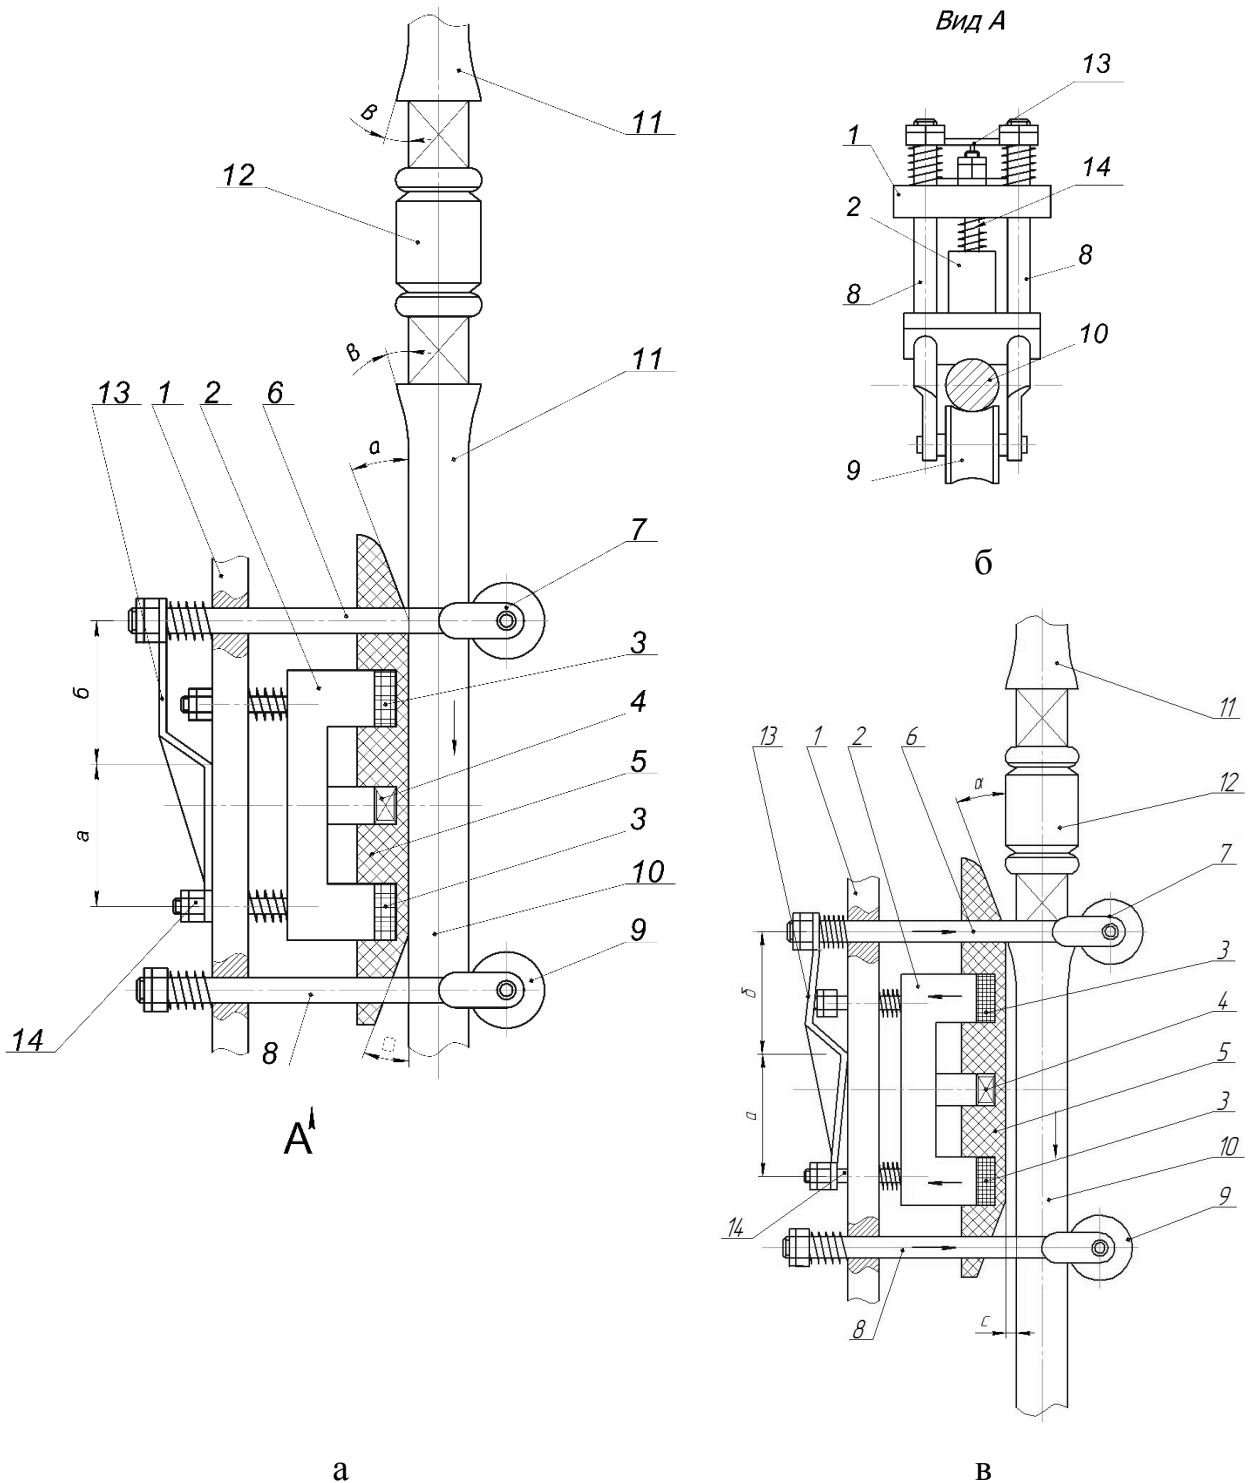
Штанговий магнітний дефектоскоп: а – робоче положення на гладкій частині штанги; б - вид А, вид знизу; в - в робочому положенні на ділянці висадженого кінця штанги
